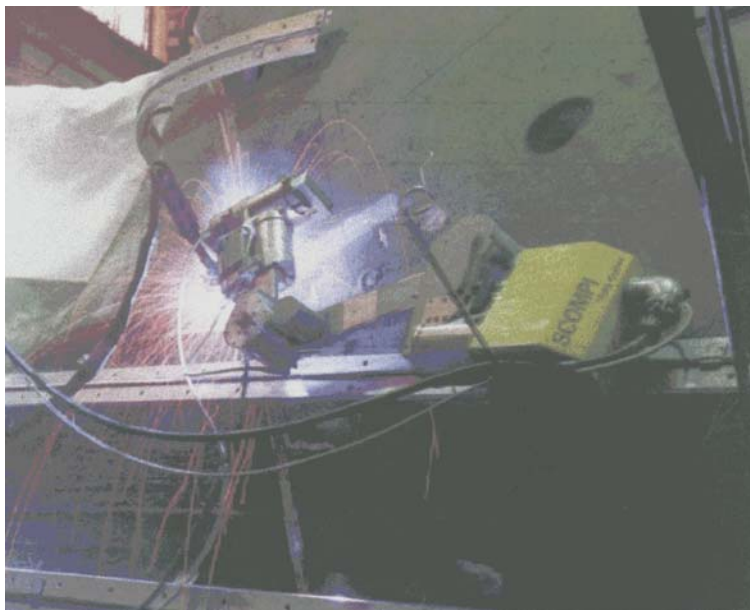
Operação de deposição robotizada por soldagem [63].
